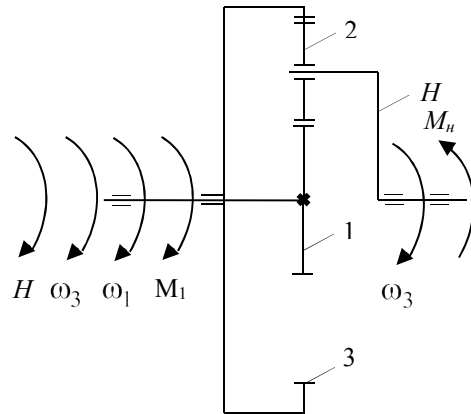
Схема планетарного механізму бортової передачі з двома ступенями свободи
